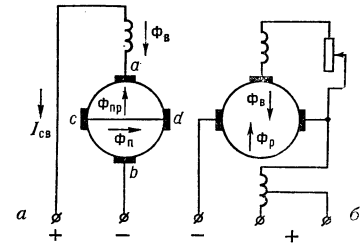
Схема сварочного генератора: а — поперечного поля; б — с размагничивающей последовательной обмоткой.
